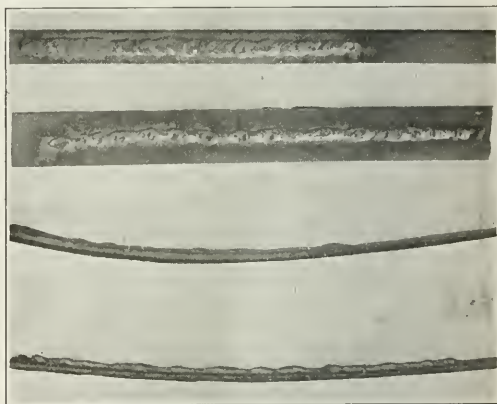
ALABEO DE LOS LADOS DE LA SOLDADURA, PRODUCIDA POR LA CONTRACCIÓN LONGITUDINAL DE LAS CAPAS DEPOSITADAS
